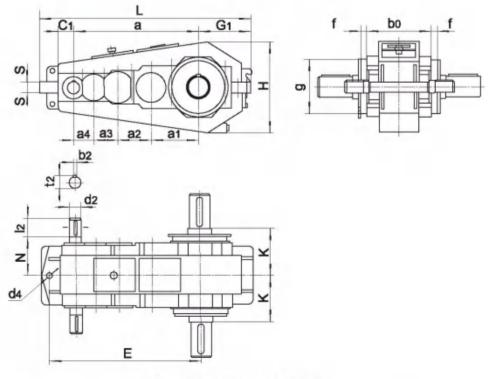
QY4S减速器外形尺寸 Figure 8 External dimension of QY4S decelerator
